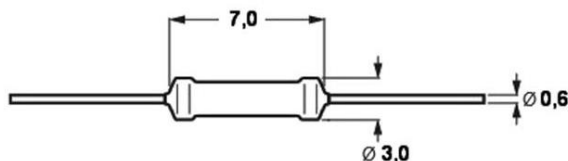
Габаритні розміри резистора MFP "Yageo"
